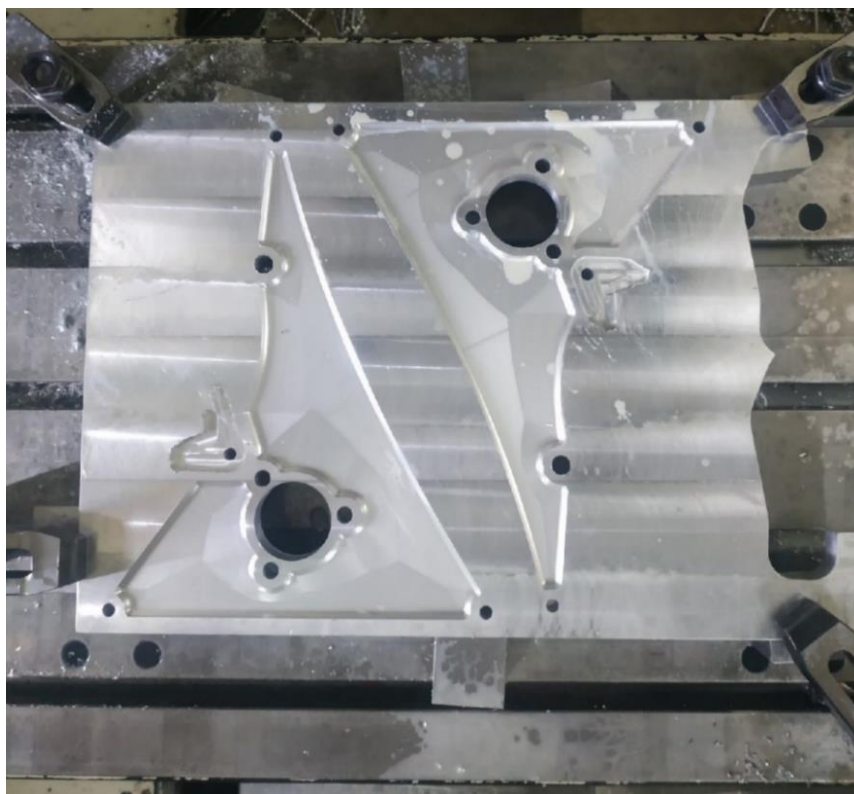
Процесс изготовления плиты на трехкоординатном фрезерном станке с ЧПУ
